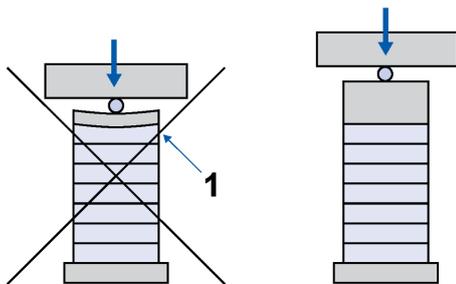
Richtiges Dimensionieren der Endstücke bei punktförmigem Kontakt (1: Zugspannungen)
